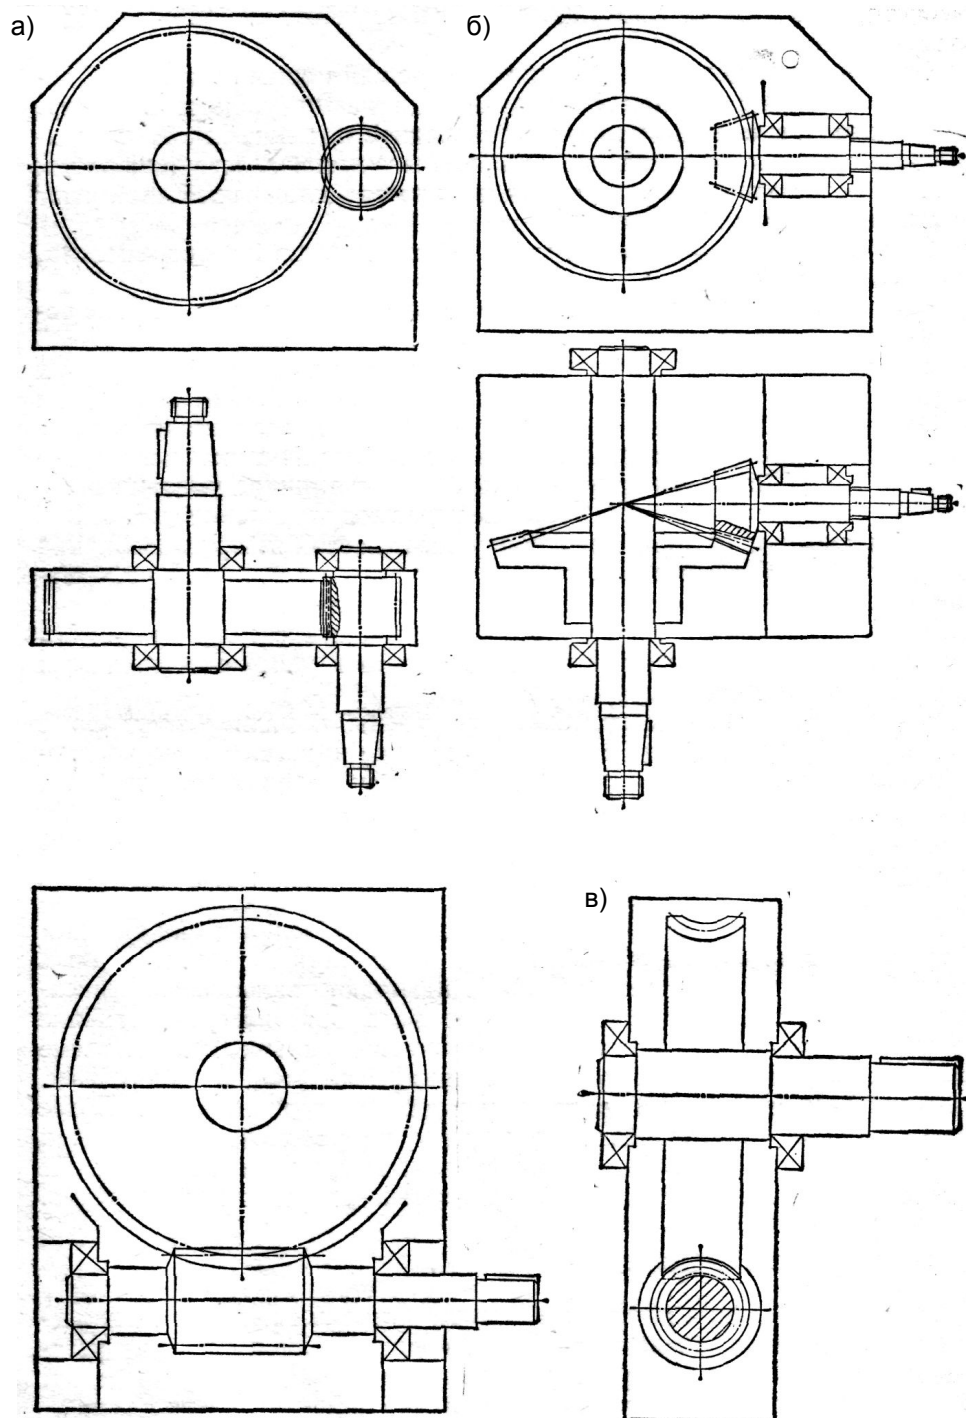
Эскизные компоновки редукторов: а) – цилиндрический; б) – конический; в) – червячный
